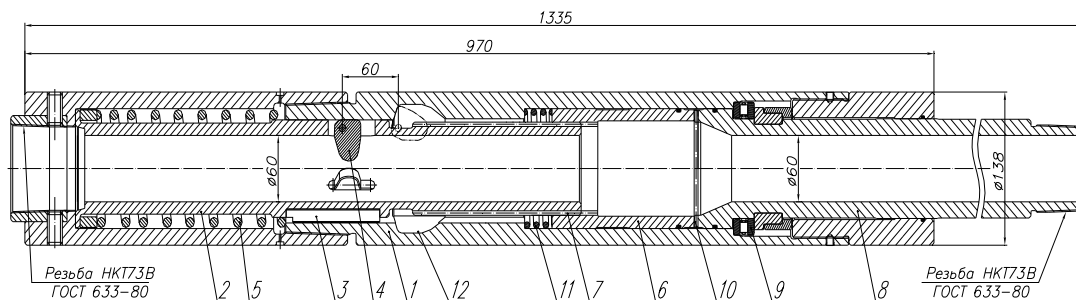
Схема механического ориентатора колтюбинговой трубы:
